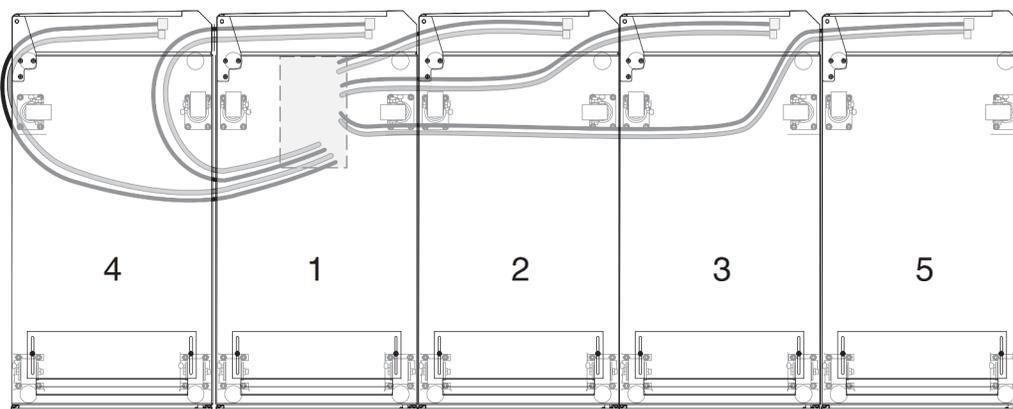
Roteamento e fixação das mangueiras em um ambiente de piso elevado para racks individuais (de cima, olhando para baixo)
